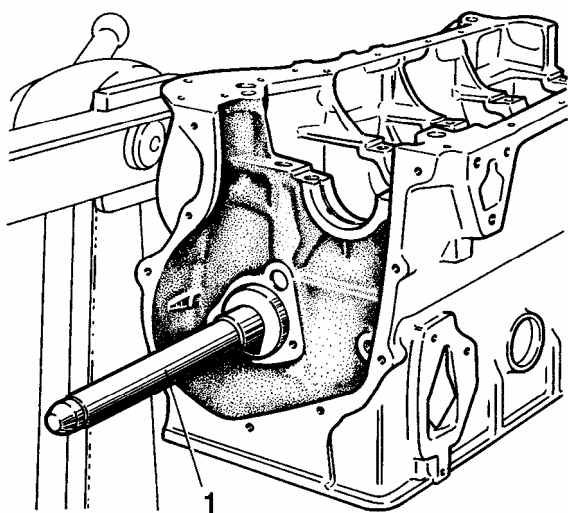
Снятие и установка втулок валика привода масляного насоса и распределителя зажигания:
